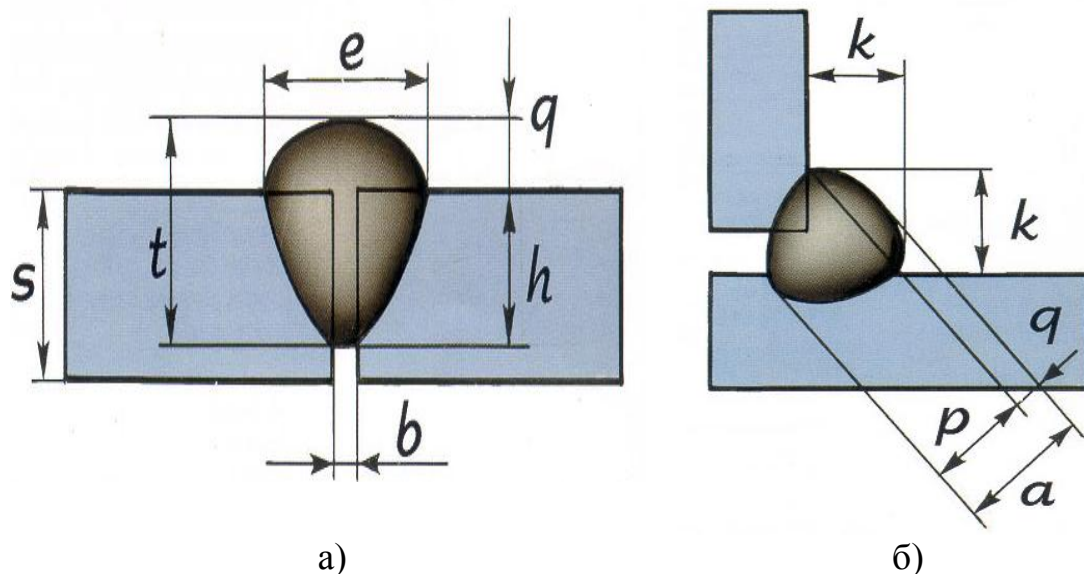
Основные геометрические параметры сварного шва:  $a$  – стыковой шов;  $b$  – угловой шов;  $a$  – толщина углового шва;  $b$  – зазор;  $s$  – толщина свариваемого металла;  $e$  – ширина шва;  $q$  – выпуклость шва;  $h$  – глубина провара;  $t$  – толщина шва;  $k$  – катет углового шва;  $p$  – расчетная высота углового шва
